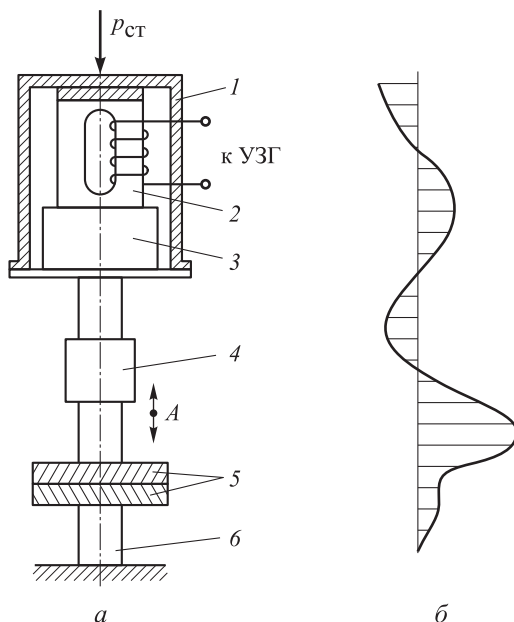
Схема установки для УЗС с нормальным вводом колебаний (а) и эпюра амплитуды колебаний колебательной системы (б): 1 — корпус преобразователя; 2 — магнитострикционный преобразователь; 3 — трансформатор упругих колебаний; 4 — волновод-инструмент; 5 — свариваемые детали; 6 — опора; А — амплитуда колебаний волновода
